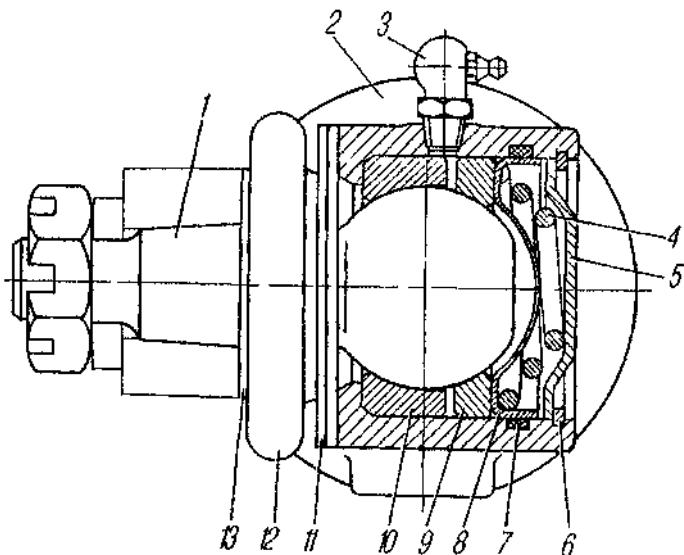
Шарнир рулевого привода: 1-палец шаровой; 2-наконечник; 3-масленка; 4-пружина; 5-заглушка; 6-кольцо стопорное; 7-уплотнитель; 8-обойма пружины; 9-вкладыш нижний; 10-вкладыш верхний; 11-накладка; 12-муфта защитная; 13-шайба
